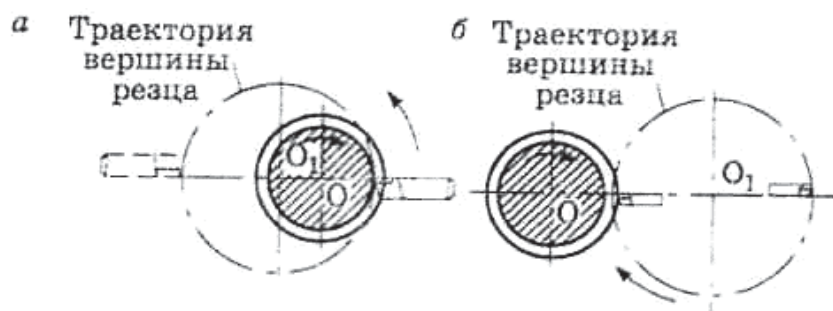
Схема нарезания резьбы вращающимися резцами (вихревой метод нарезания резьбы); O-O<sub>1</sub> – расстояние между осями вращения детали и резца
